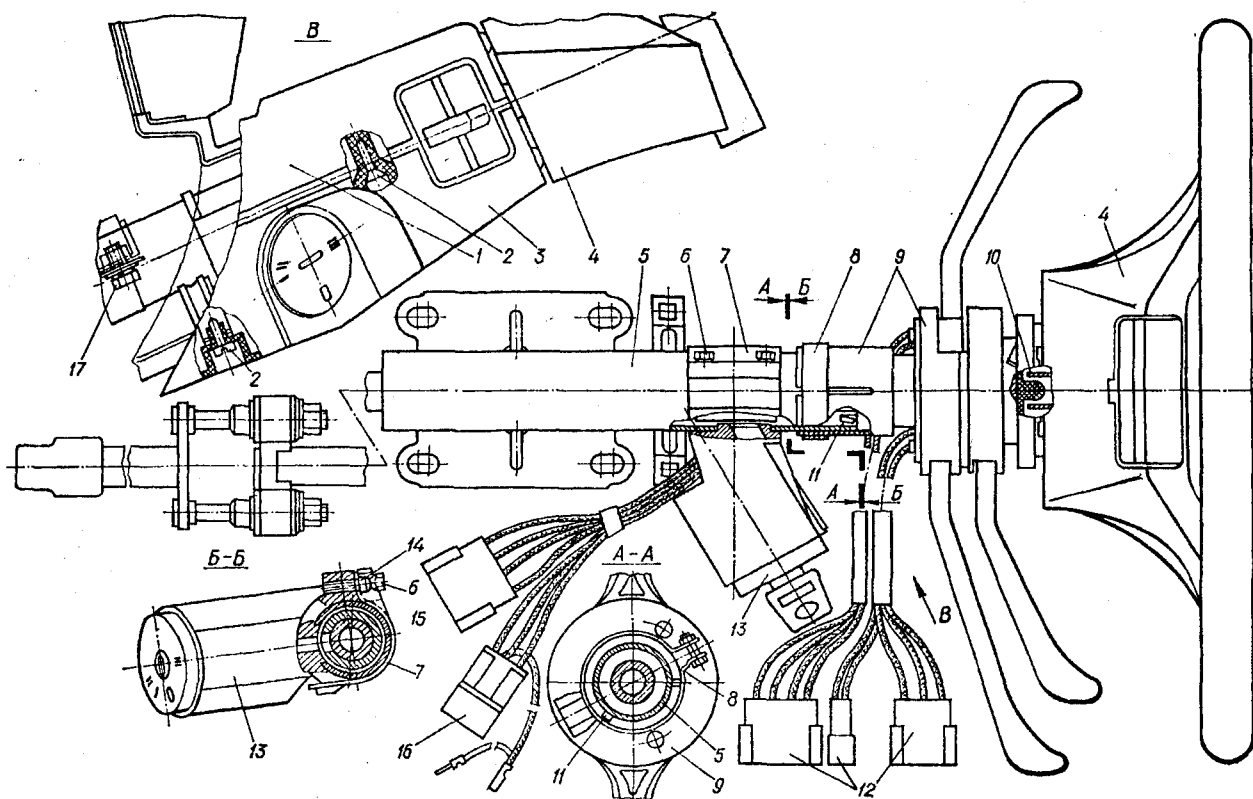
Опора вала в сборе с выключателем зажигания, рулевым колесом и переключателем: 1 – кожух верхний; 2 – винты крепления кожухов; 3 – кожух нижний; 4 – колесо рулевое; 5 – опора вала; 6 – головка болта крепления выключателя зажигания; 7 – скоба выключателя зажигания; 8 – хомут; 9 – переключатель в сборе; 10 – выступ на кольце сбрасывателя (на переключателе поворотов); 11 – выступ на опоре вала (ограничитель глубины установки переключателя на опору); 12 – штекерные колодки переключателя; 13 – выключатель зажигания; 14 – специальный болт крепления выключателя зажигания; 15 – штекерная колодка подключения выключателя зажигания к основному жгуту проводов; 16 – реле выключателя зажигания (может не устанавливаться); 17 – болт крепления опоры
